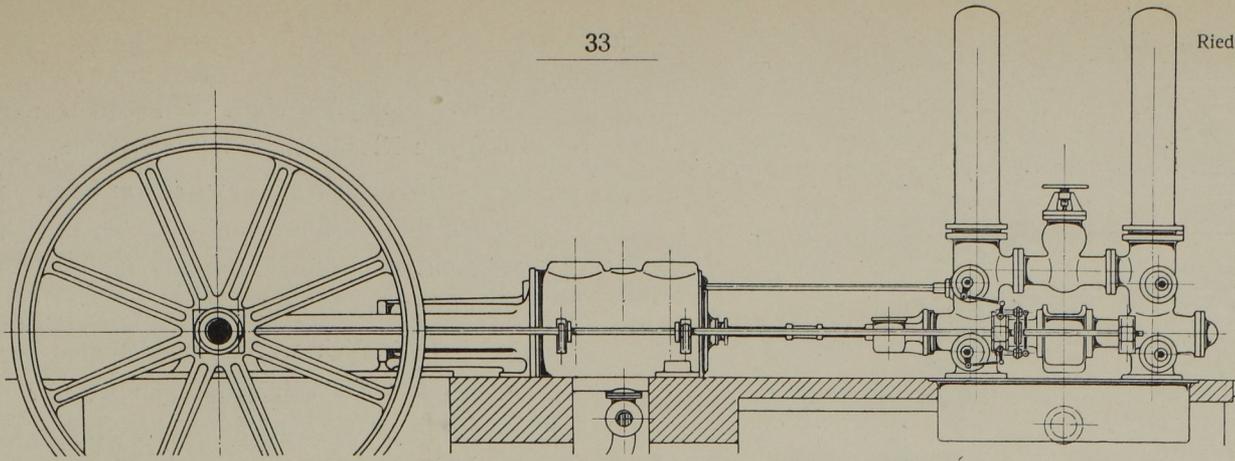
Seitenansicht der Pumpmaschine. Masst. 1:80.
